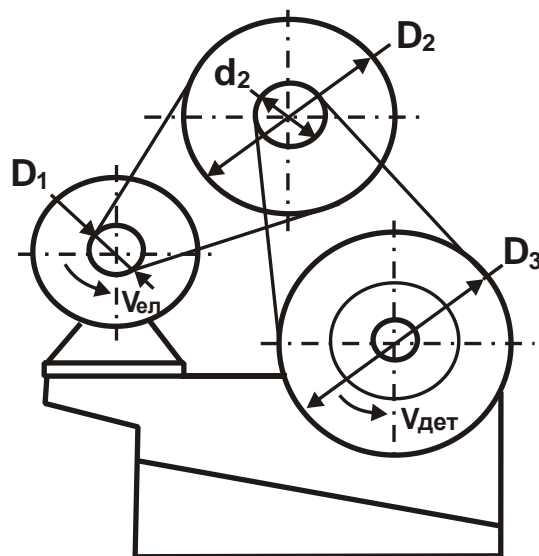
Схема формувальних рухів оброблюваної деталі на верстаті
